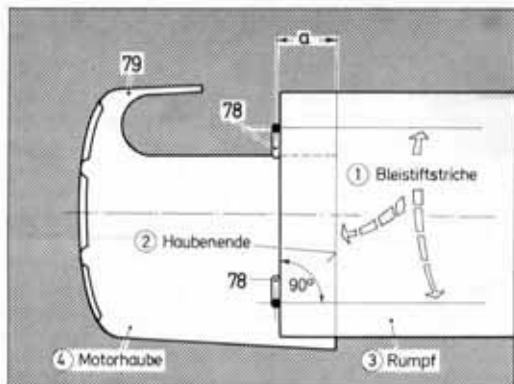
Das Anzeichnen der Mittelpunkte der Bohrungen für die Befestigungsschrauben der Motorhaube.
